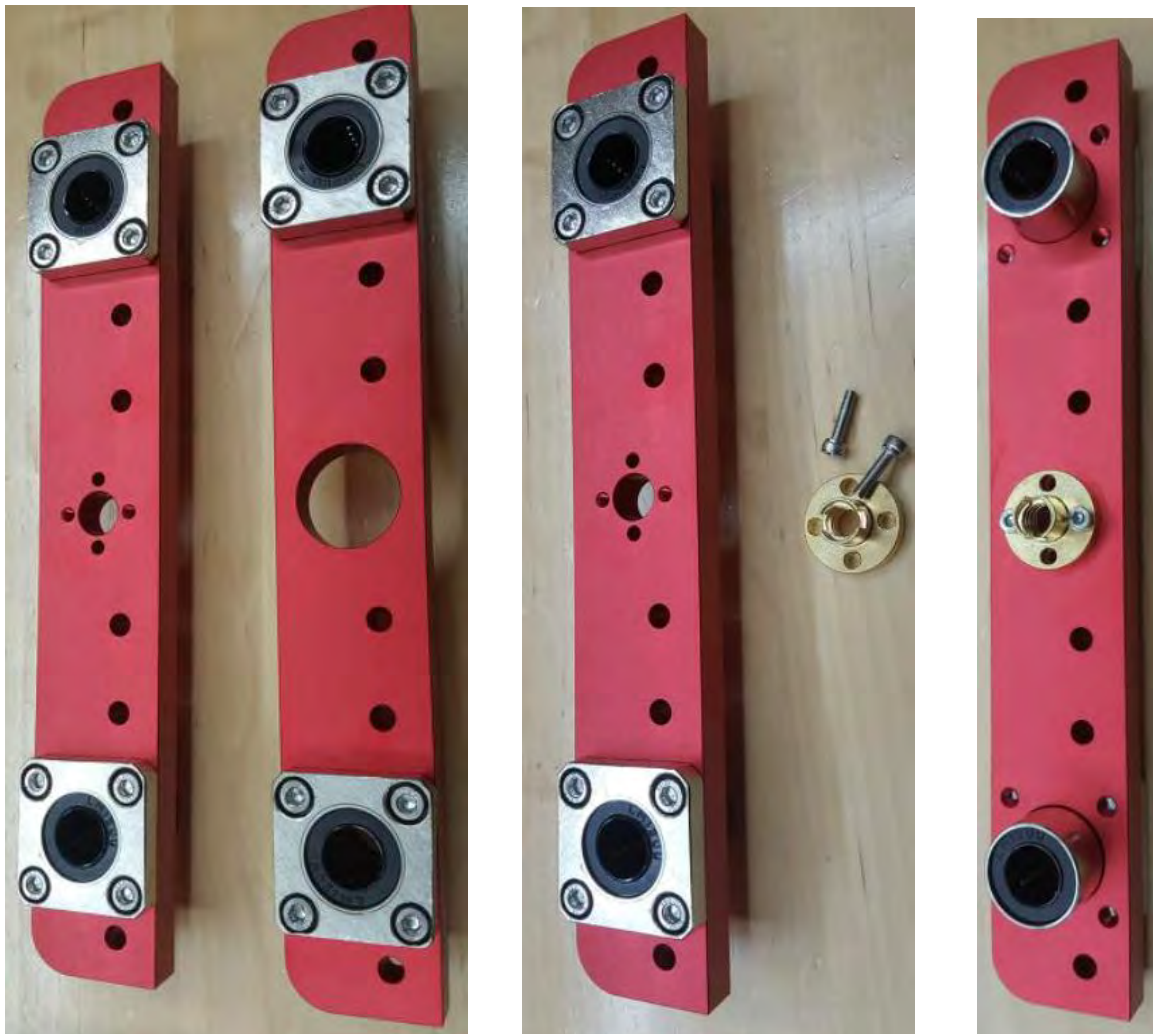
Ensamble de cojinetes y tuerca en placa de eje Y
